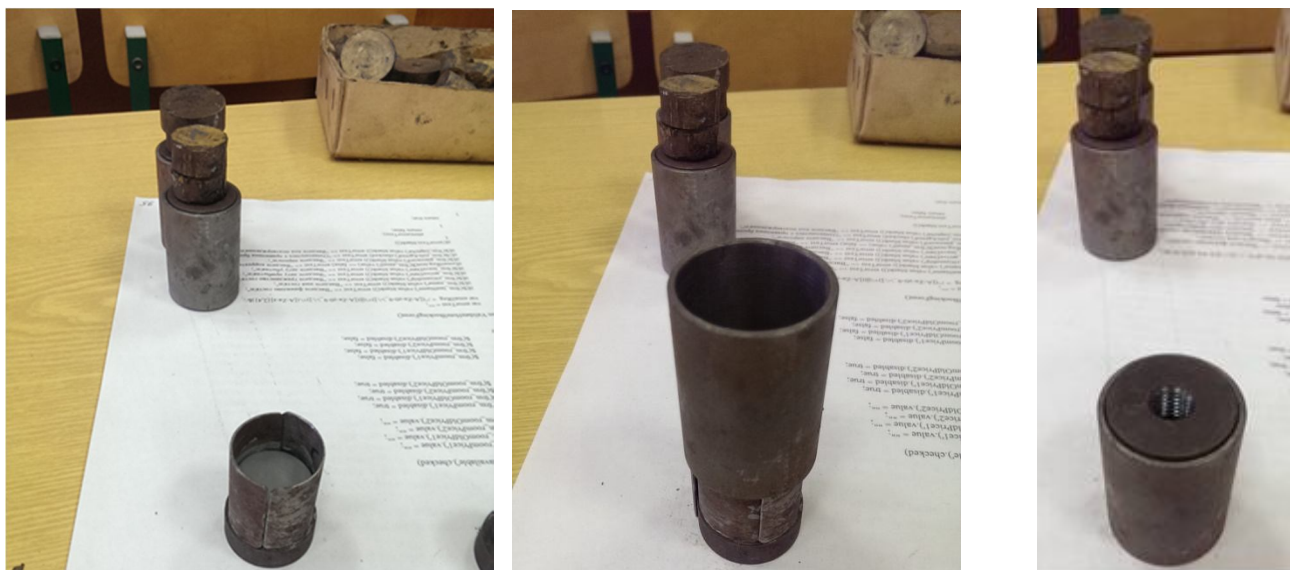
Сборка образца с гарантированным зазором для испытаний на отрыв
